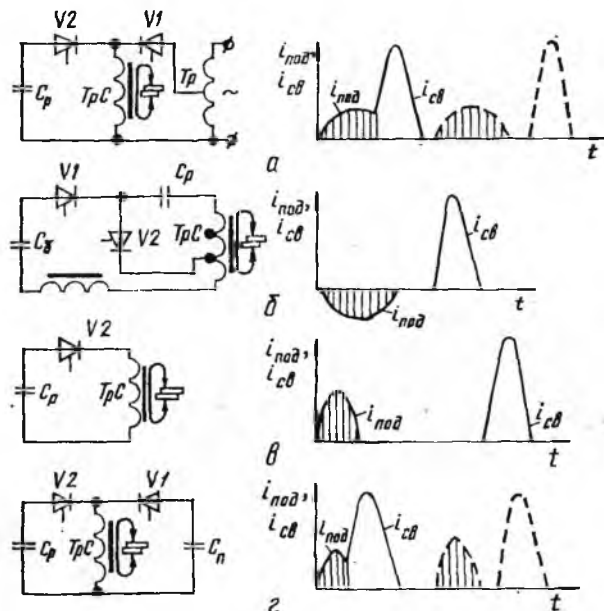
Схемы, обеспечивающие предварительный подогрев зоны контактной сварки ($V1$, $V2$ — управляемые вентили).
